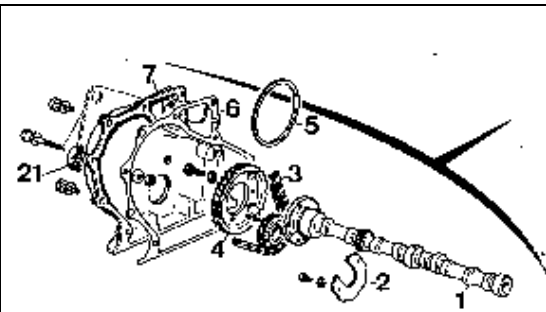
Fixation de l'arbre à cames en tête : 2 – bride de fixation
